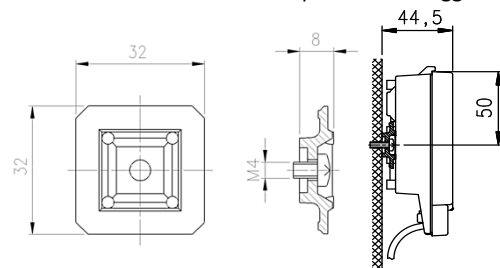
Piastra di fissaggio e fissaggio a parete.
